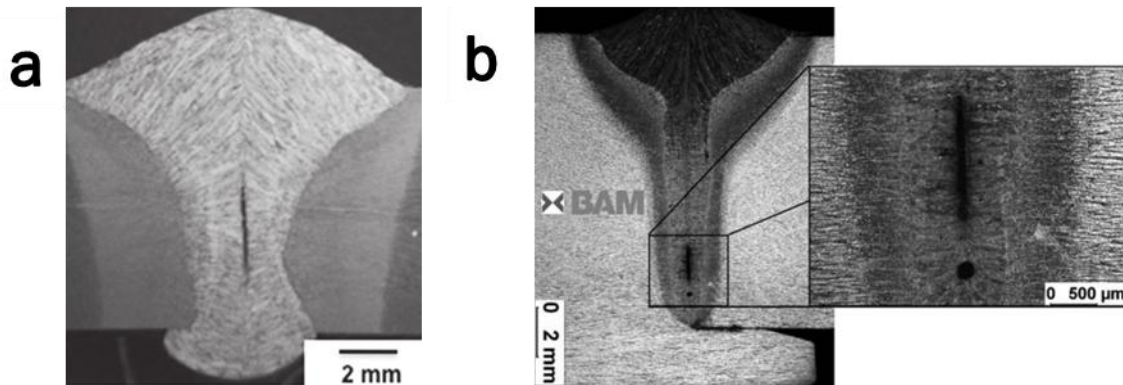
Fissuration de solidification dans un acier en soudage MAG tandem [151] et en soudage hybride laser-MAG [150]
